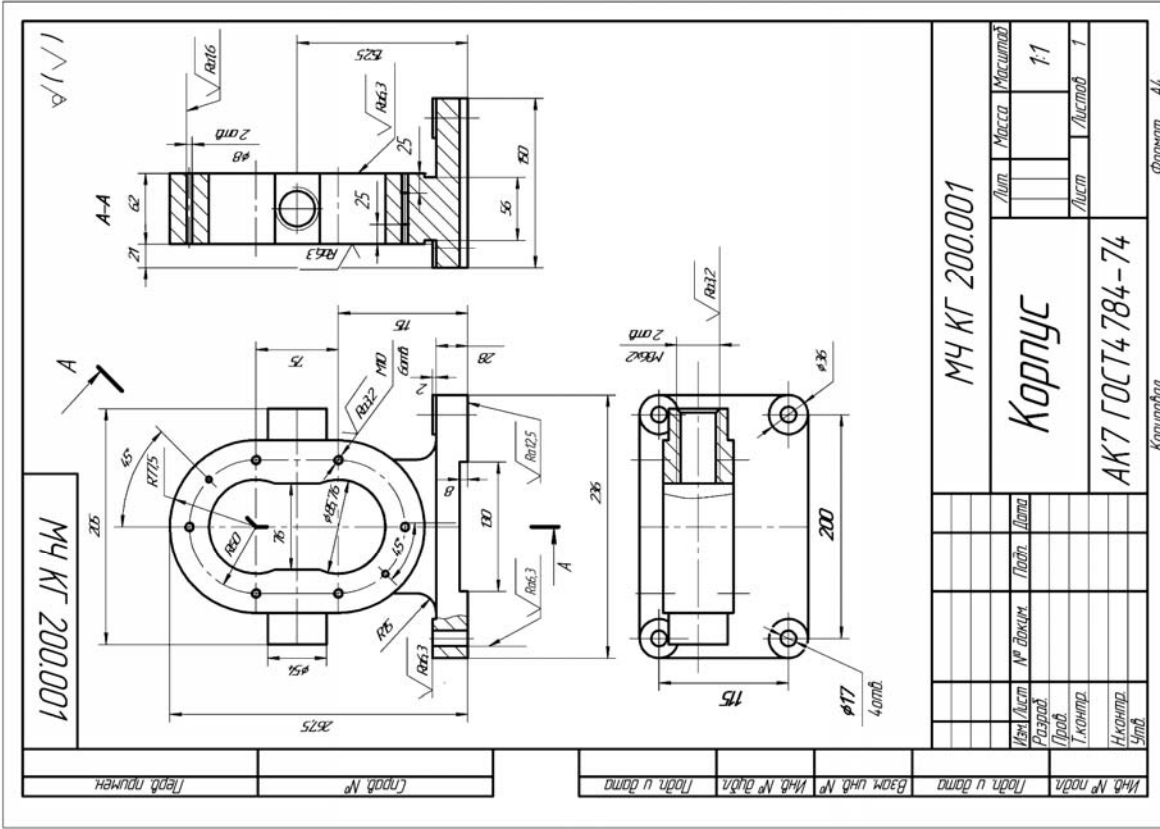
Рабочий чертеж «Корпус», позиция 1
